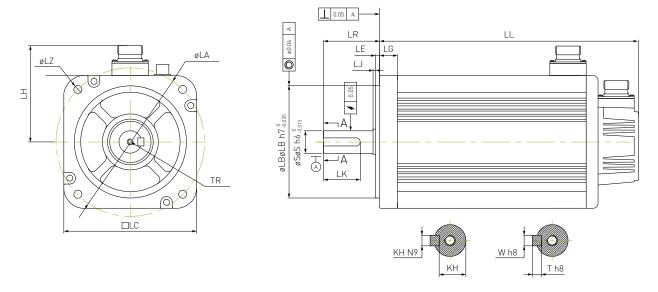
Габаритные размеры серводвигателя ELM2H-xxx (380VAC).
